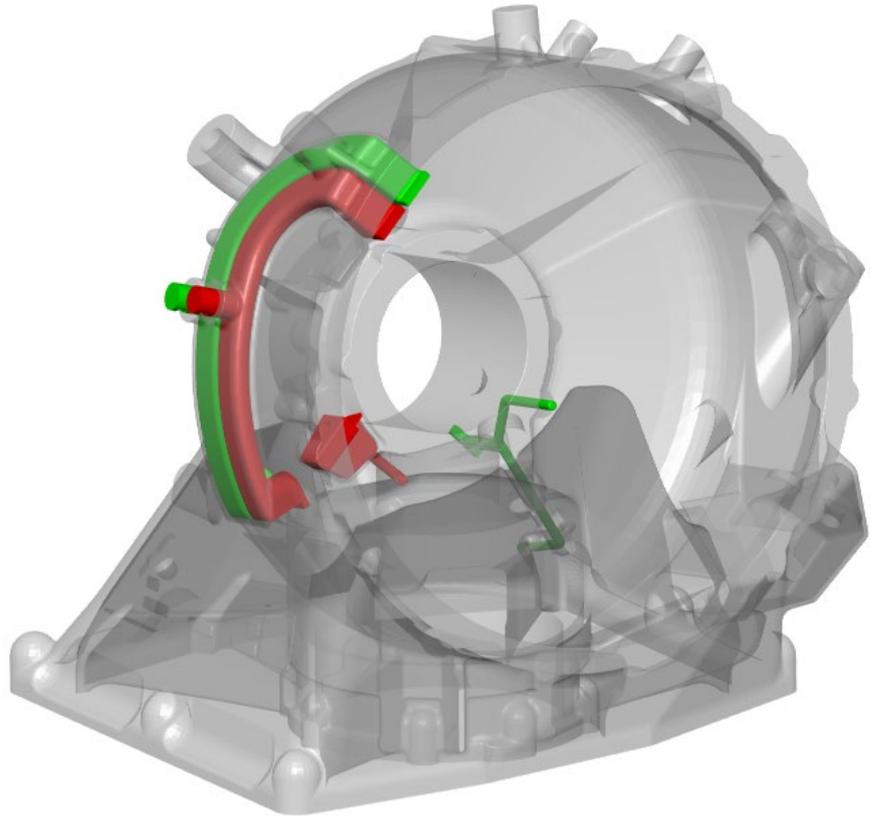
Gussgehäuse für einen Heckrotor, Programm NH 90, Größe 520 x 500 x 460 mm, Gewicht 26 kg, incl. keramische Kerne
